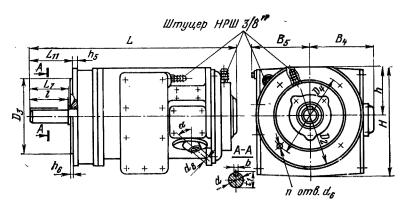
Габаритные и установочные размеры электродвигателей с водяным охлаждением АРФВ 5 и 6-го габаритов.
